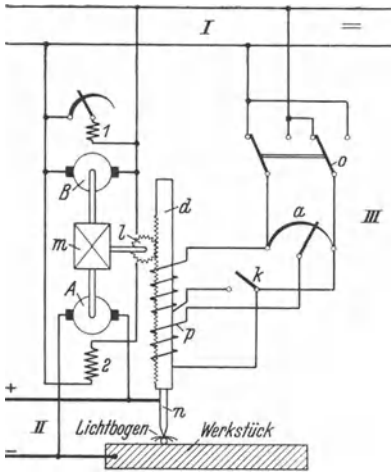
Steuerung eines Kohlebogens-Schweißautomaten.
